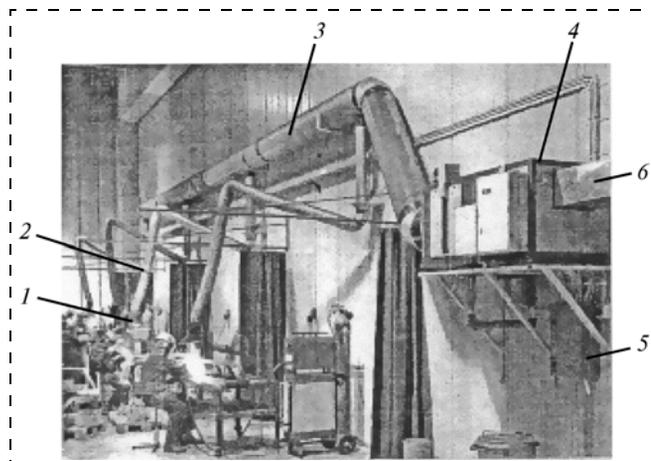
Участок ручной сварки с сухой очисткой сварочного дыма:
